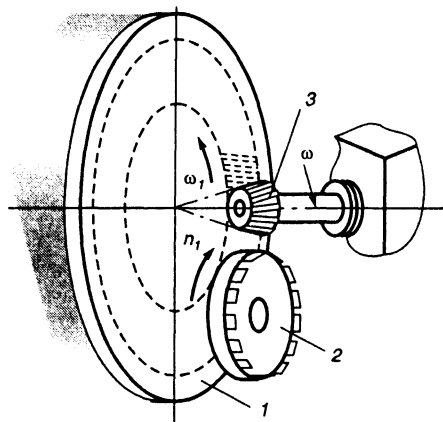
Нарезание конического колеса с криволинейными зубьями
